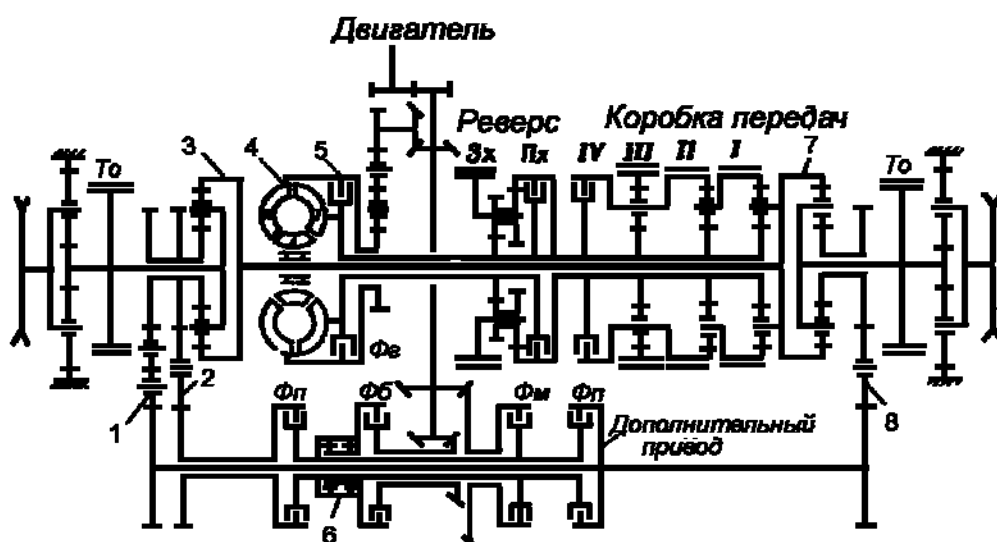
Кинематическая схема гидромеханической трансмиссии танка «Леопард»:
